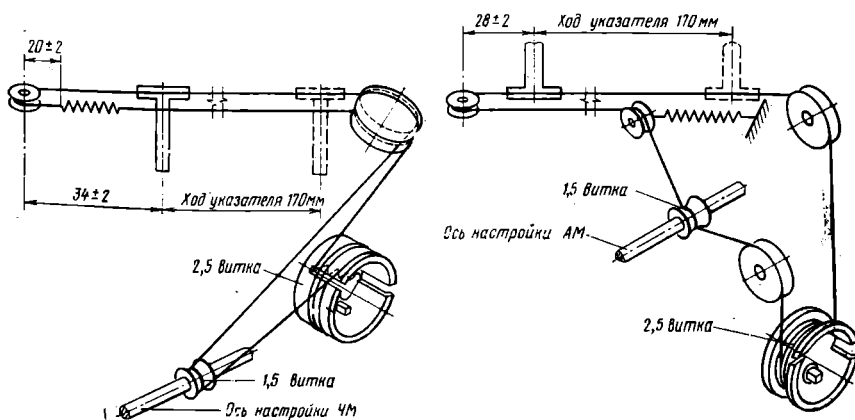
Кинематическая схема верньерного устройства радиол «Вега-315» и «Вега-321-стерео»
